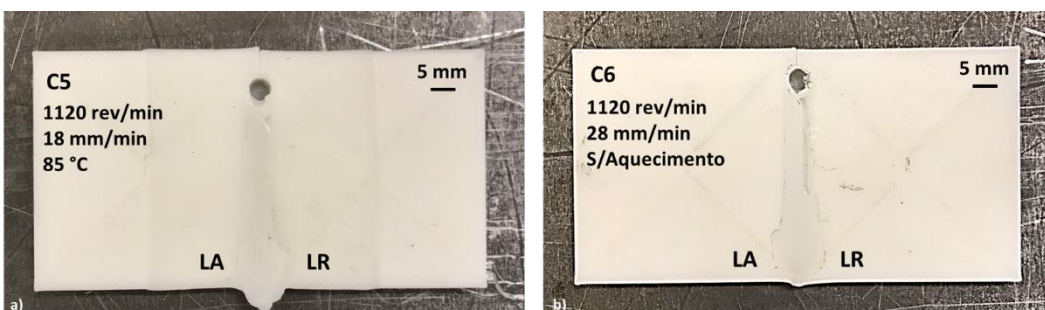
Aspeto visual da superfície das placas soldadas com combinação de parâmetros 5 e 6.
